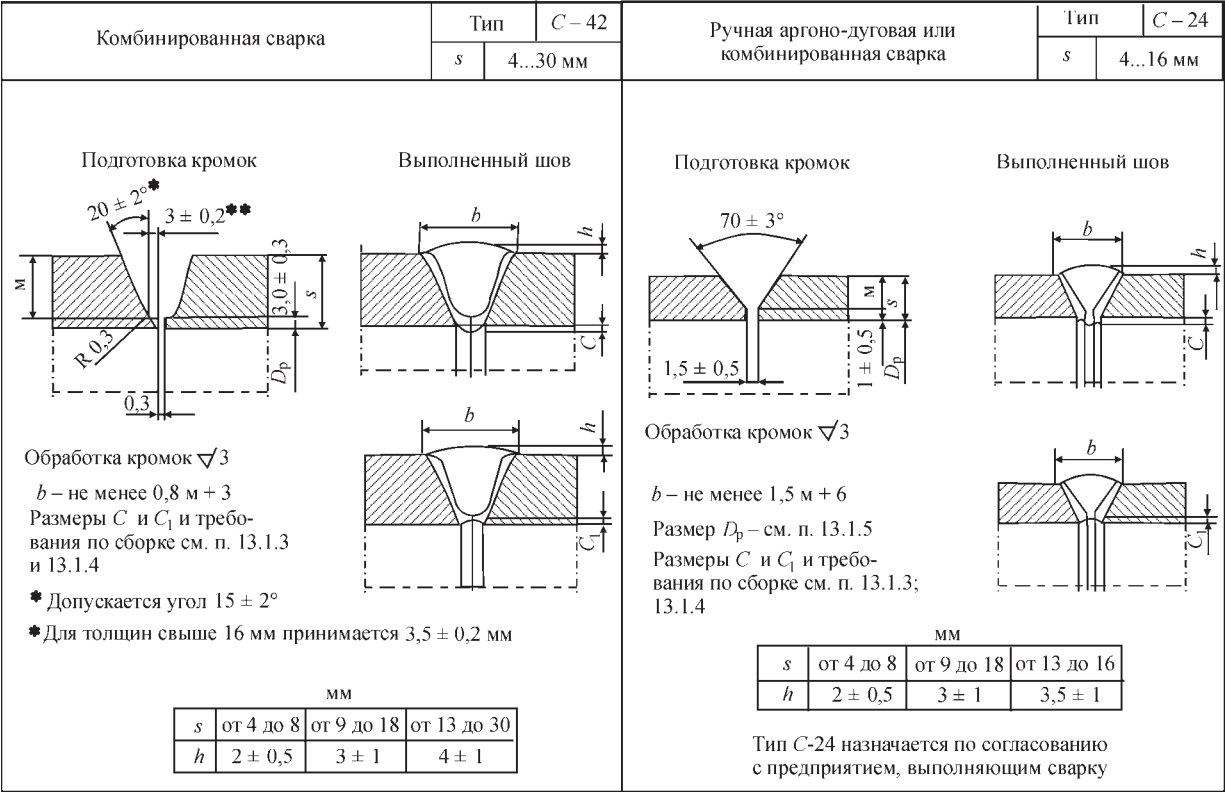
Конструкции сварных соединений трубопроводов Ду-300 в соответствии с рекомендациями ОП 1513-72 и ПНАЭГ-7-09-89
